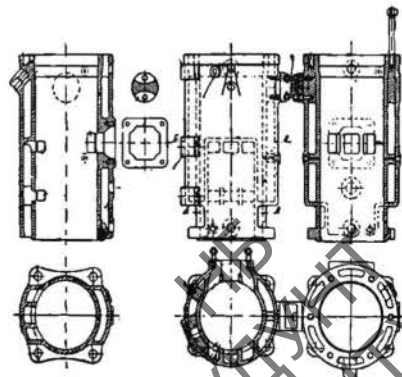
Цилиндр двухтактного двигателя Кертинга.
